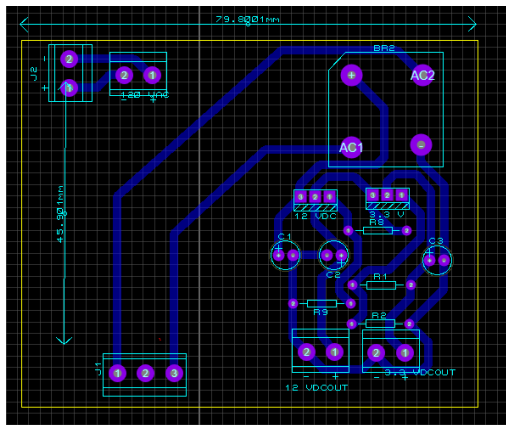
, Diseño PCB Fuente en Proteus. Fuente: elaboración propia de los autores
